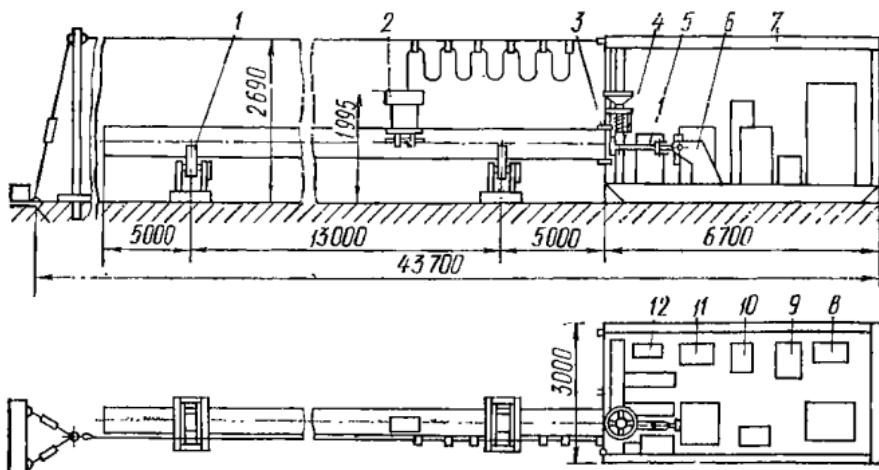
Установка УСТ-1420 для сварки труб в плети:
